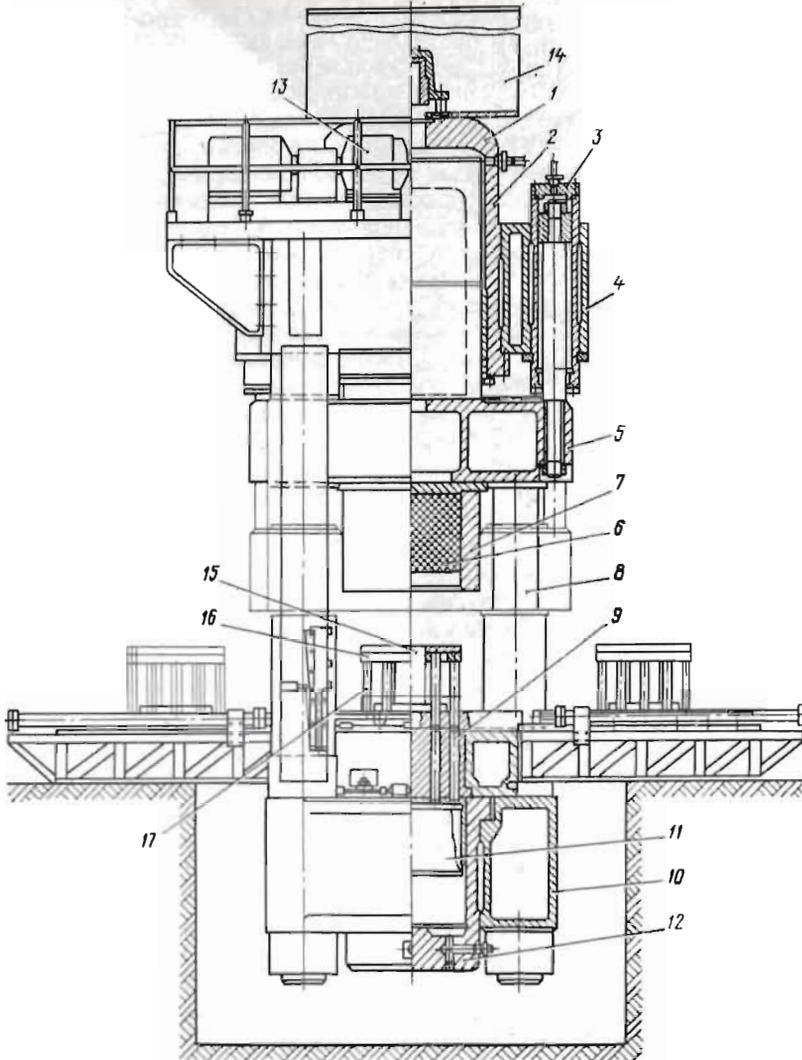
Пресс штамповки-вытяжки резиной ПШВР-3
